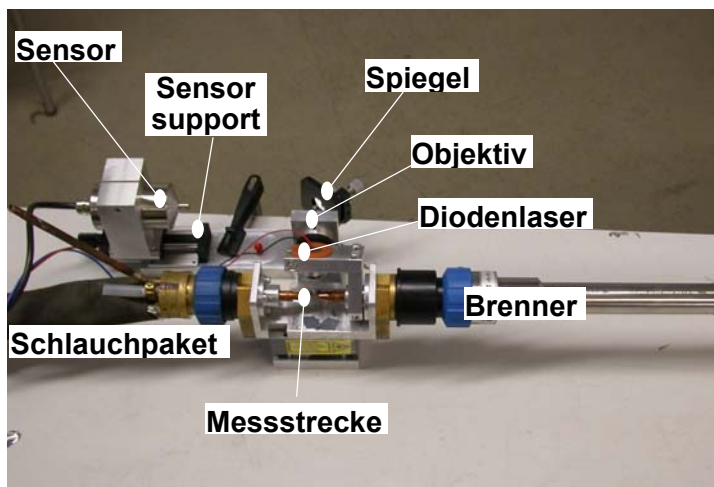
Roboter-Schweißbrenner mit optischer Geschwindigkeitsmessung
